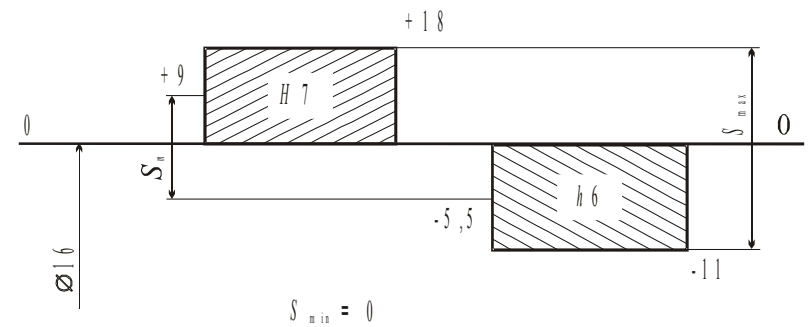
Схема расположения полей допусков отверстия и вала
